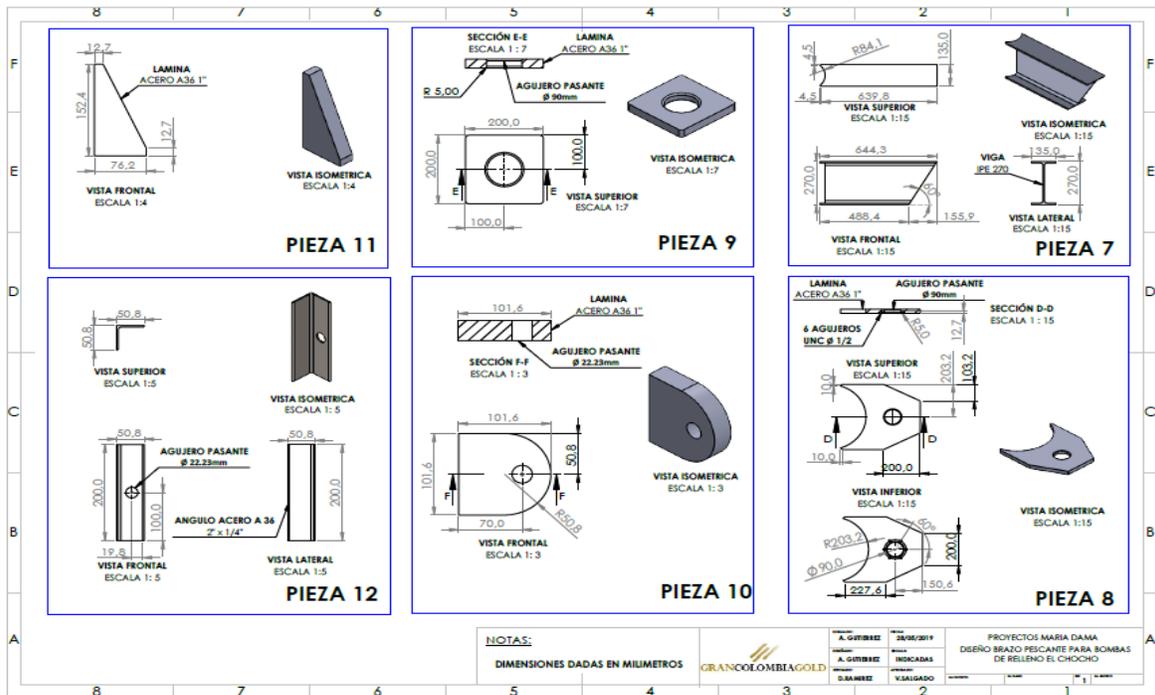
Plano #2 de piezas brazo pescante (Autoría Propia)
